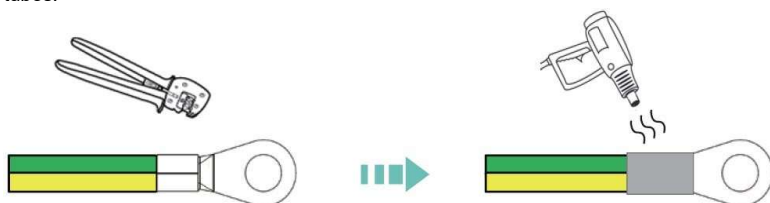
Crimpagem e vedação do cabo de aterramento
